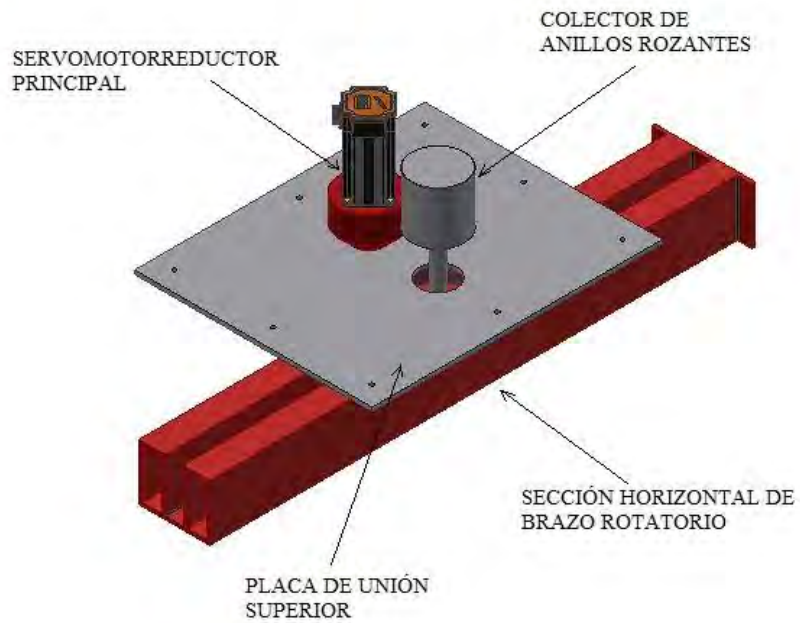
Estructura horizontal de brazo giratorio. Fuente: Propia.
